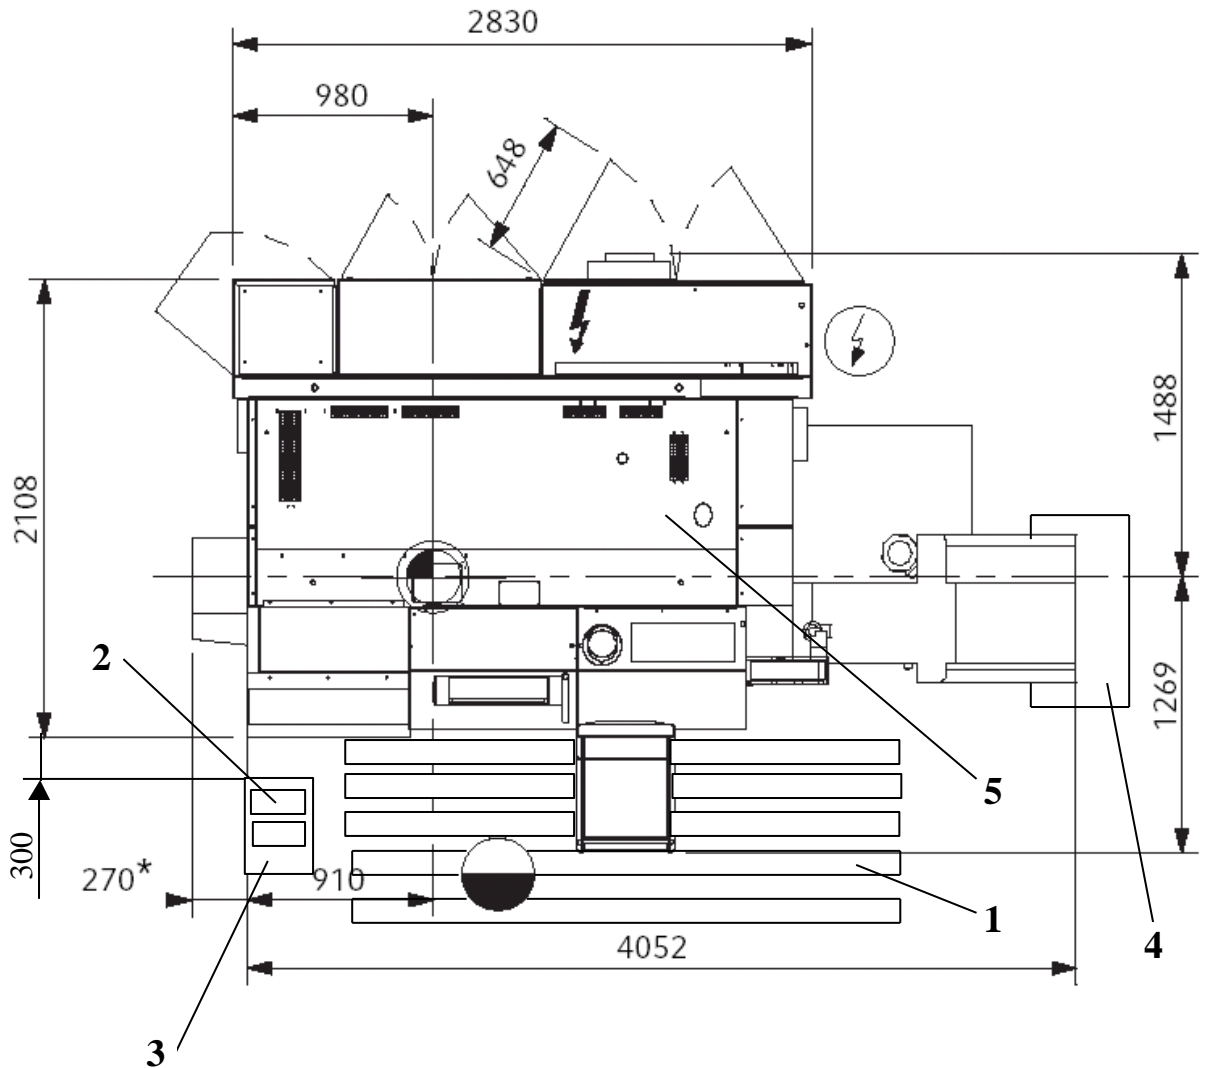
Планування робочого місця оператора проектного верстата:
